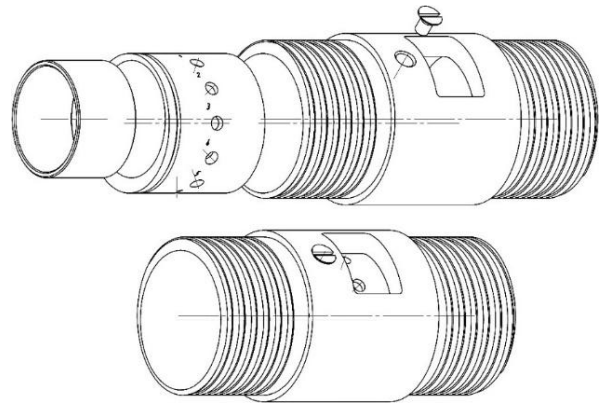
Узел искривления ведущего вала в разборе (сверху) и в сборе (снизу)
